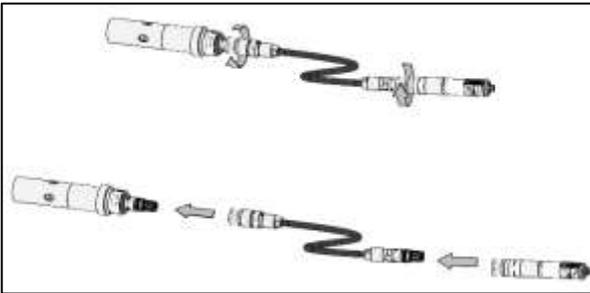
Beispiel für die Kabelbefestigung zwischen Sensor und SA11
